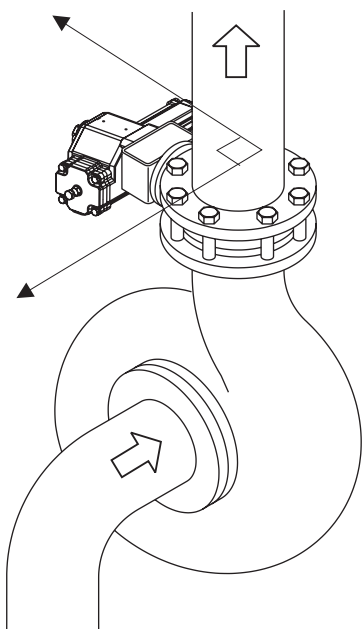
Instalar a válvula de borboleta após uma bomba centrífuga
